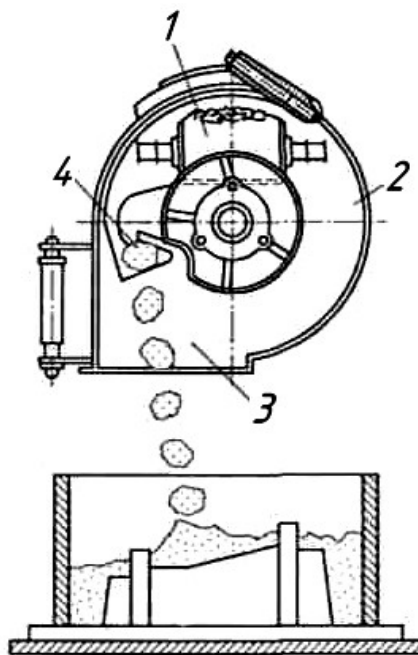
Схема действия метательной головки пескомета: 1 – ленточный конвейер для подачи смеси; 2 – кожух головки; 3 – пакет смеси в выходном отверстии; 4 – сменная лопатка (ковш)
